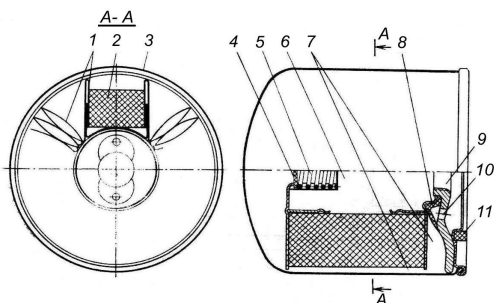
Комбинированный масляный фильтр автомобиля ВАЗ: 1, 2 – основной и дополнительный фильтрующие элементы; 3 – корпус фильтра; 4 – перепускной клапан; 5 – пружина; 6, 7 – центральная и наружная кольцевые полости; 8 – противодренажный клапан; 9 – резьбовое отверстие; 10 – впускные отверстия; 11 – уплотнительное кольцо.
